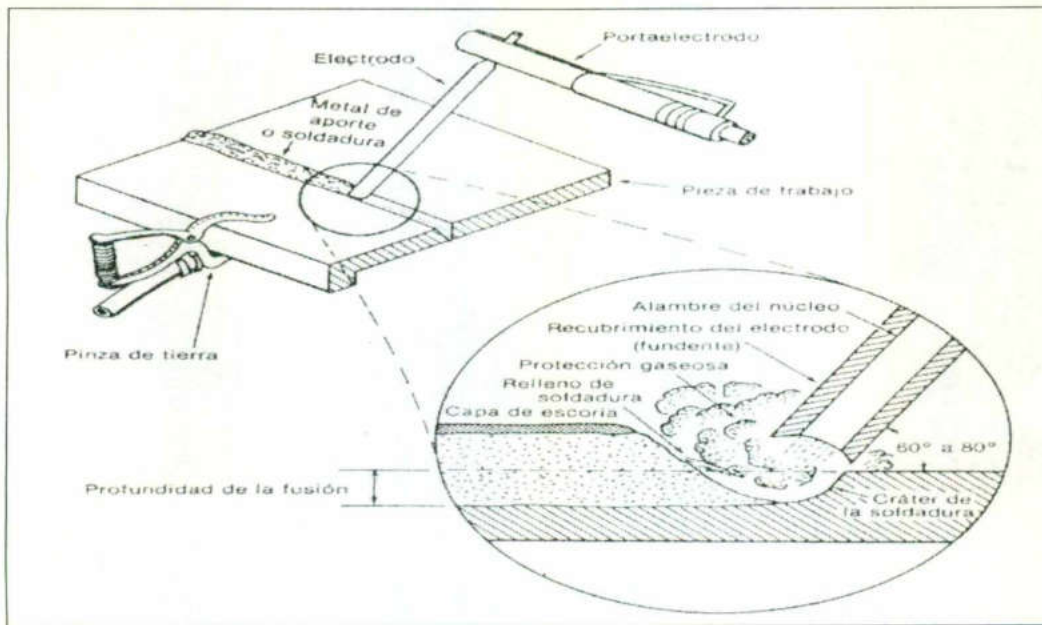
Proceso de soldadura por arco (Horwitz, 2002)
